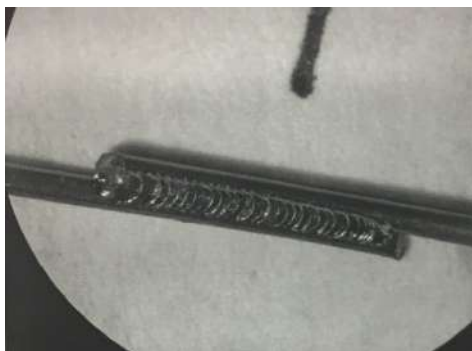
Вид соединения нитиноловой проволоки внахлест лазерной сваркой
